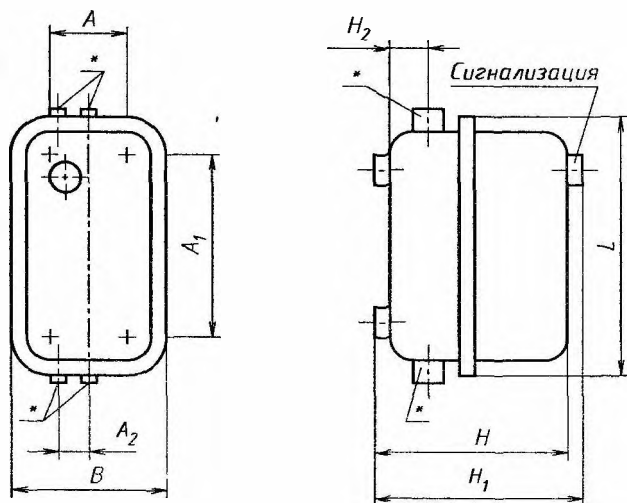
Габаритные и установочные размеры реверсивных пускателей ПМЛ 3-й и 4-й величин в оболочке
